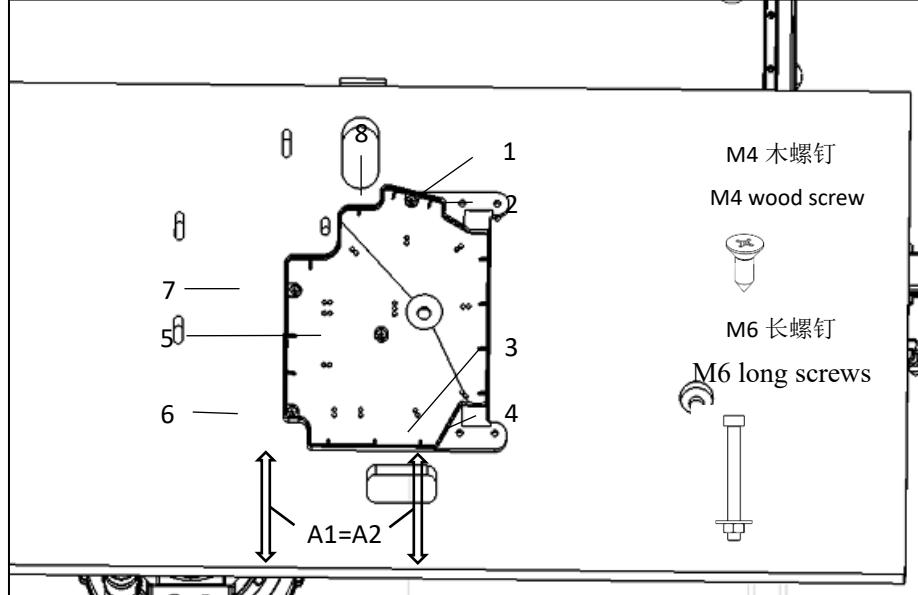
油盘安装图 Figure 9/2 Oil pan installing drawing
